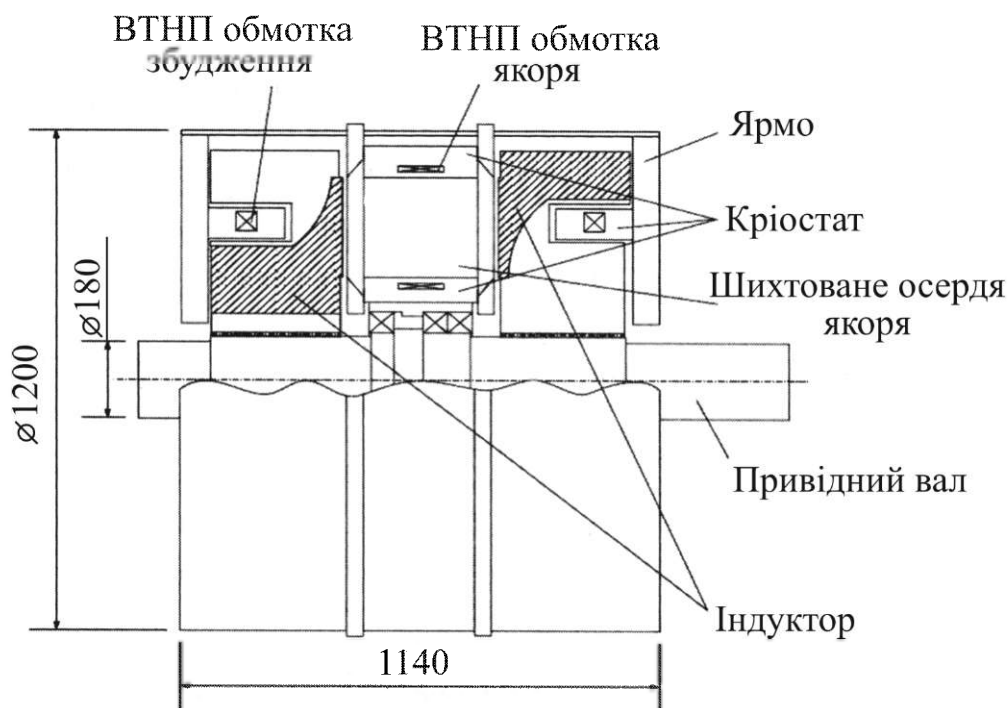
Конструктивна схема ВТНП двигуна індукторного типу
